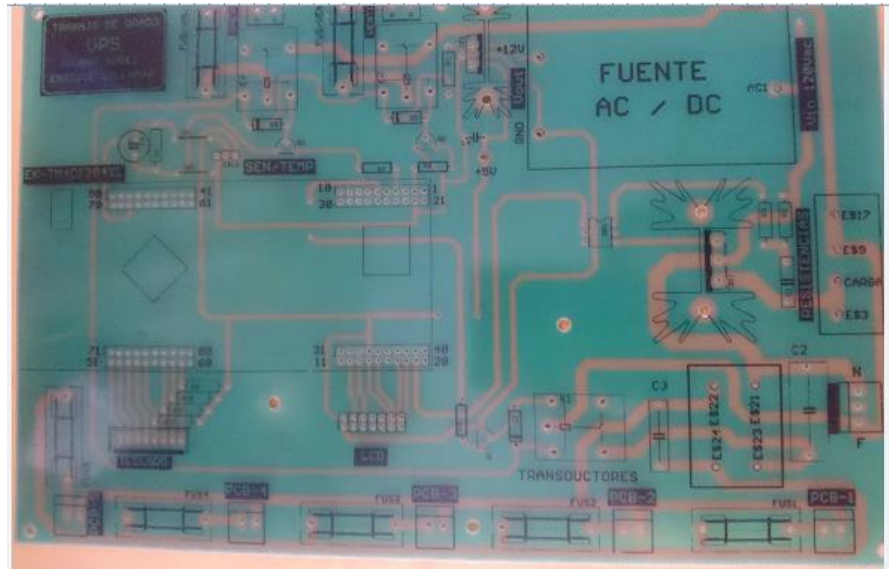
Vista superior de placa de circuitos PCB interfaces construida.
